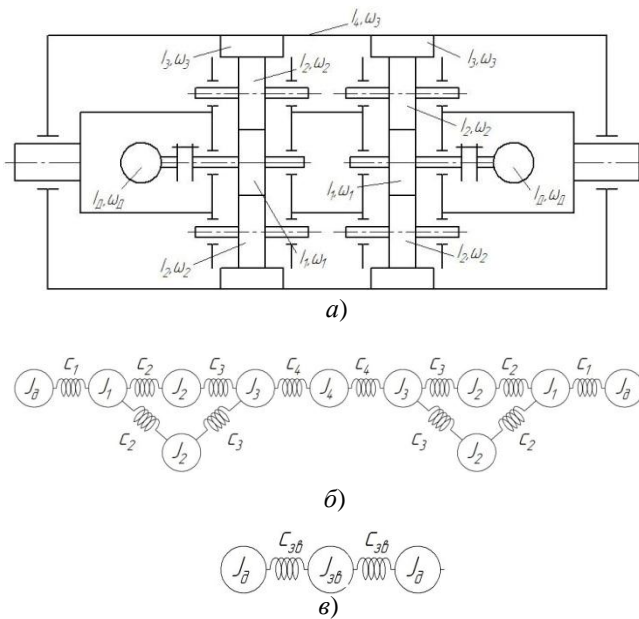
Розрахункова схема механічної частини гідралічного вмонтованого привода (а), зведена одинадцятимасова системи з дванадцятьма пружними зв'язками (б), розрахункова схема механічної частини (в)
